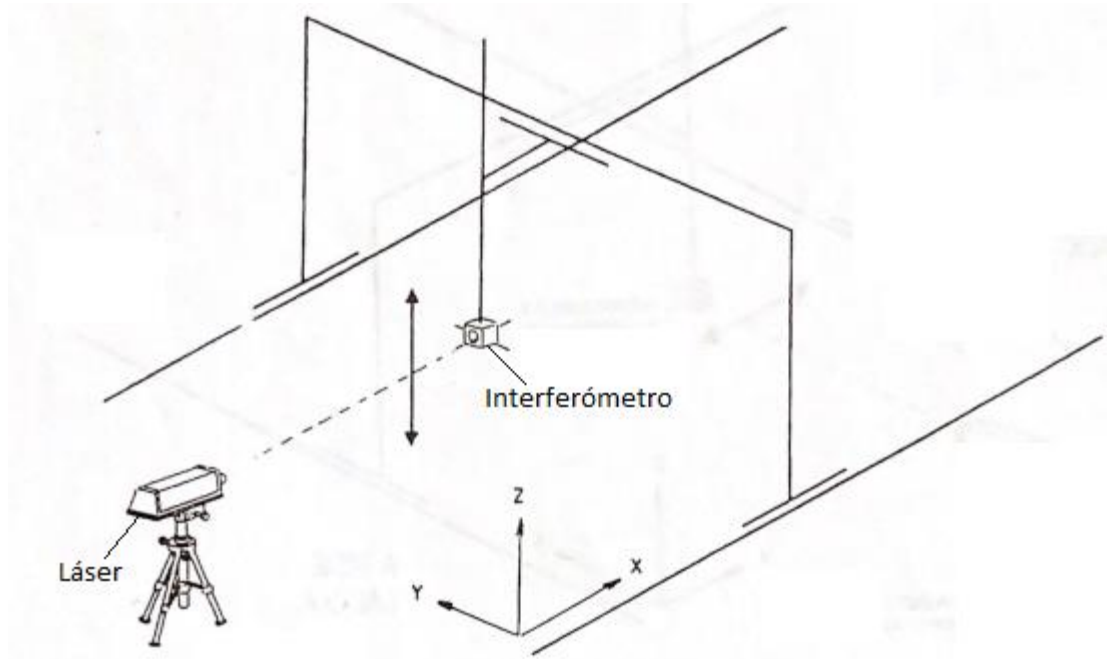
Esquema montaje ensayo de rectitud en plano vertical
